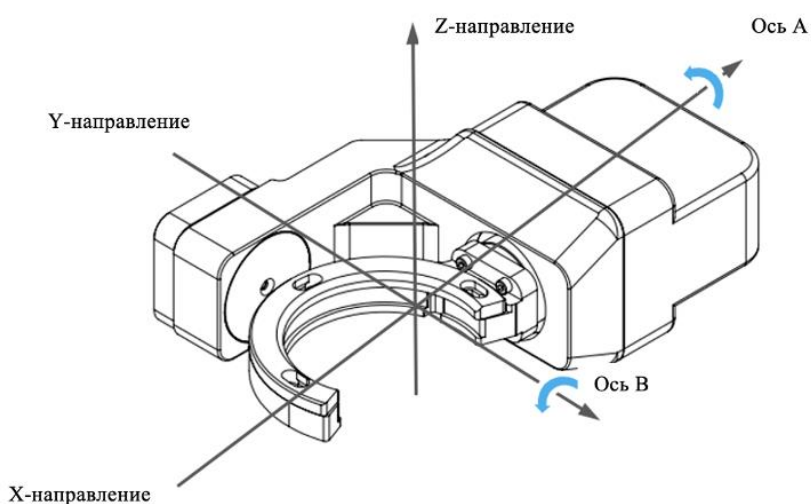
Оси фрезерования и вращения держателя (на примере С-держателя) для 5-осевых станков
